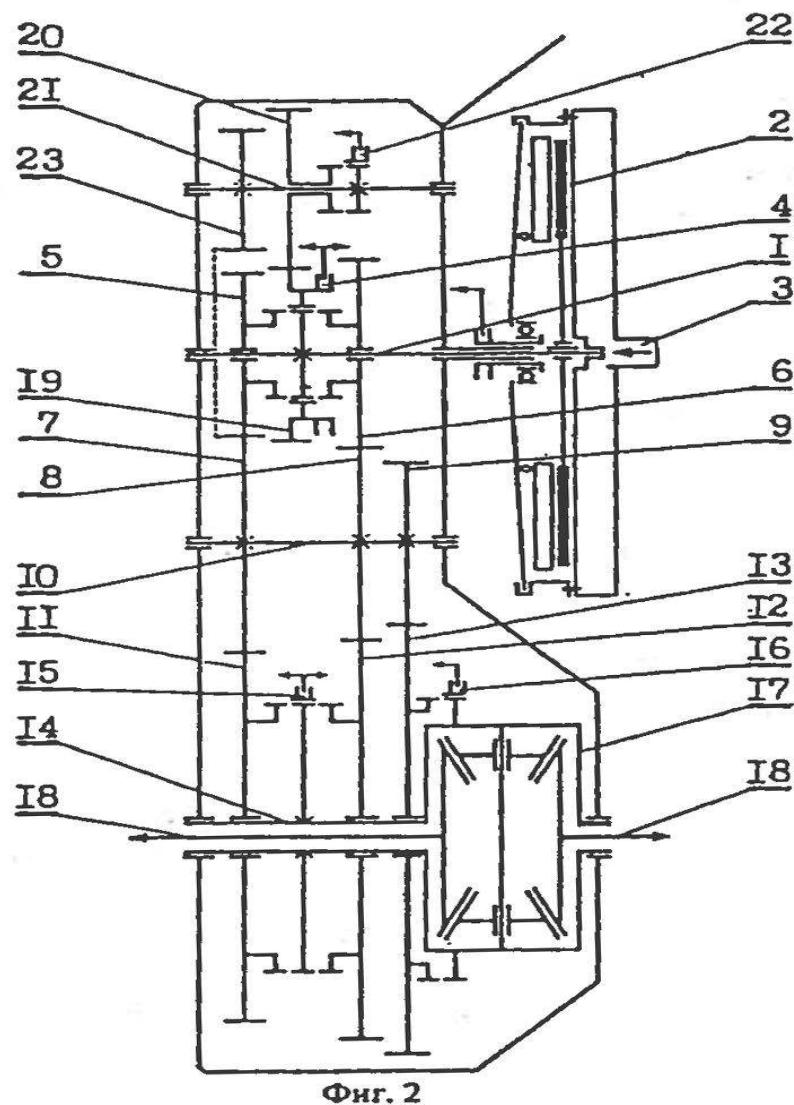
Кинематическая схема экспериментальной коробки передач с муфтой блокировки одного из зубчатых колес
